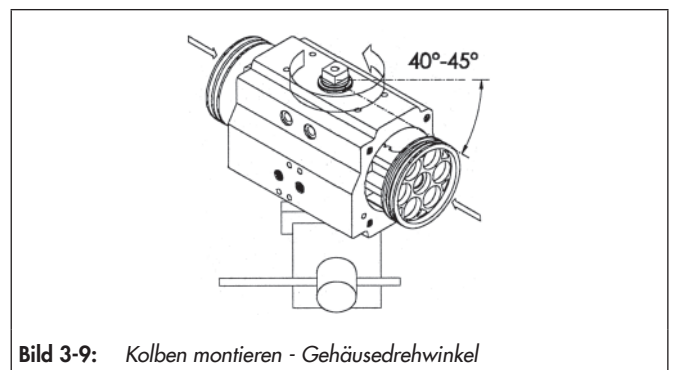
Kolben montieren - Gehäusedrehwinkel
